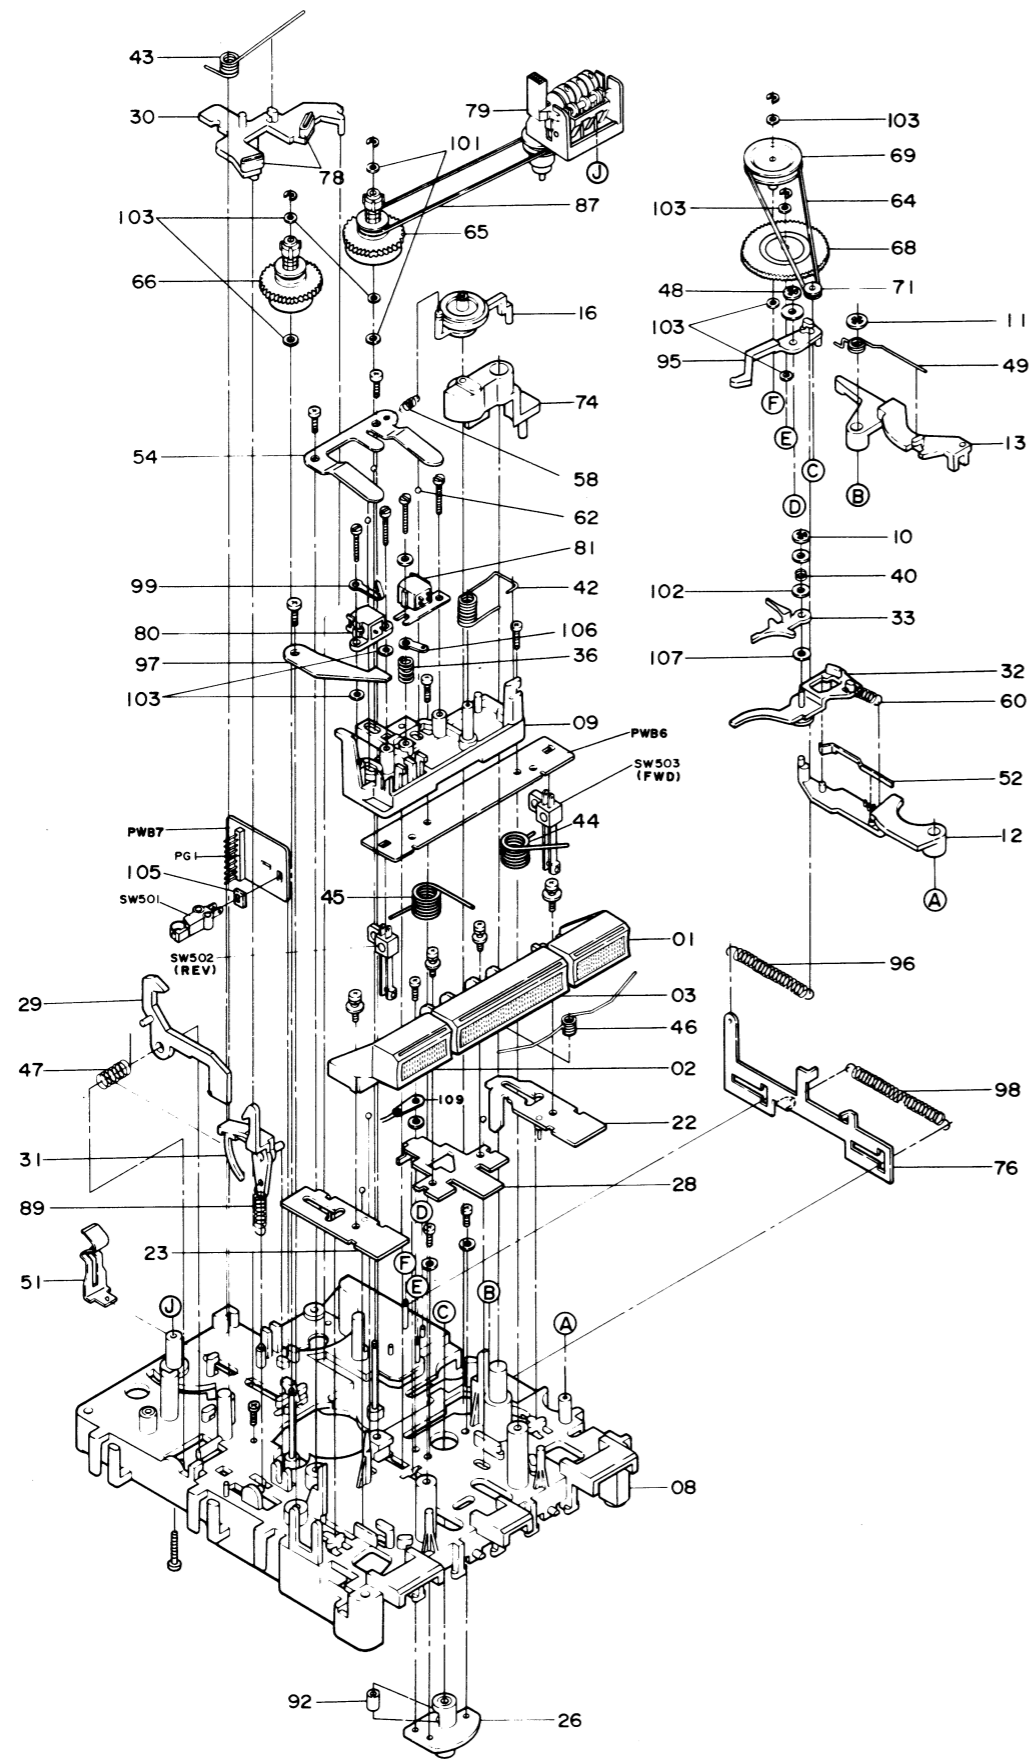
EXPLOSIONSDARSTELLUNG DES MECHANISMUS (DRAUFSICHT)
